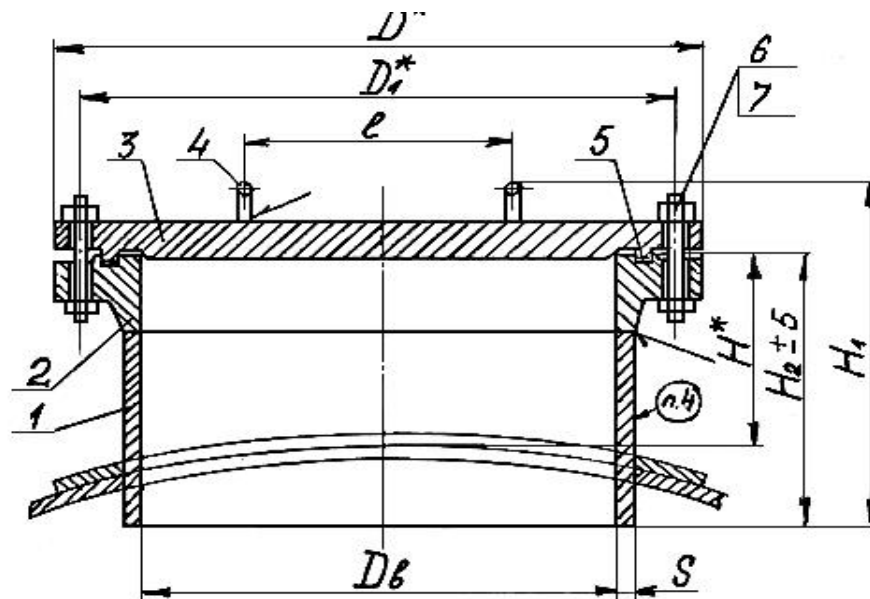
Люк-лаз с фланцами, приварными встык, с уплотнительной поверхностью "шип-паз"
